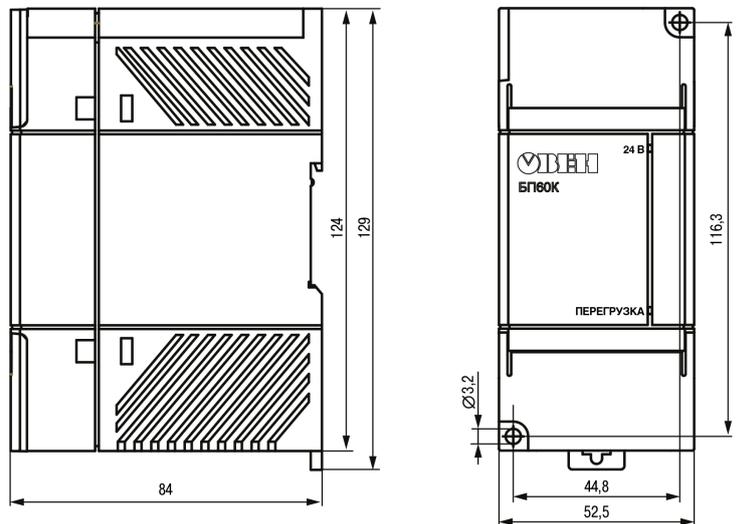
Внешний вид, габаритные и установочные размеры прибора
